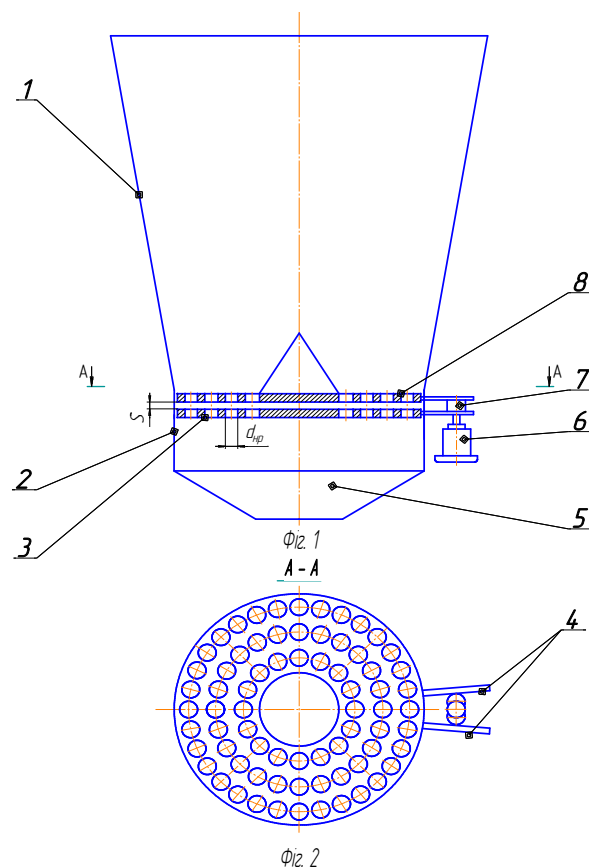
Решетчатый дозатор концентрированных кормов: 1 – наддозаторный конический бункер; 2 – цилиндрический корпус; 3 – нижнее
